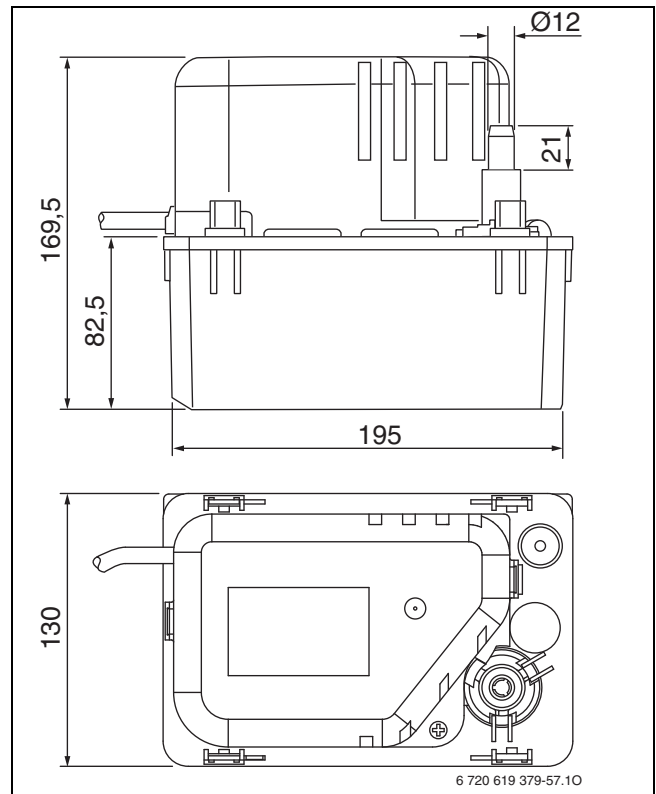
Abmessungen Nr. 1620 (Maße in mm)
